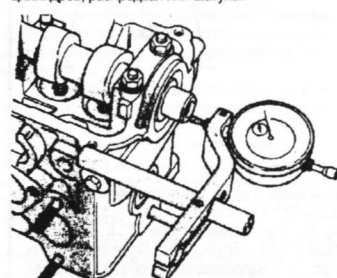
Для того, чтобы проверить конечный люфт распредвала, присоедините измерительный прибор подобным
